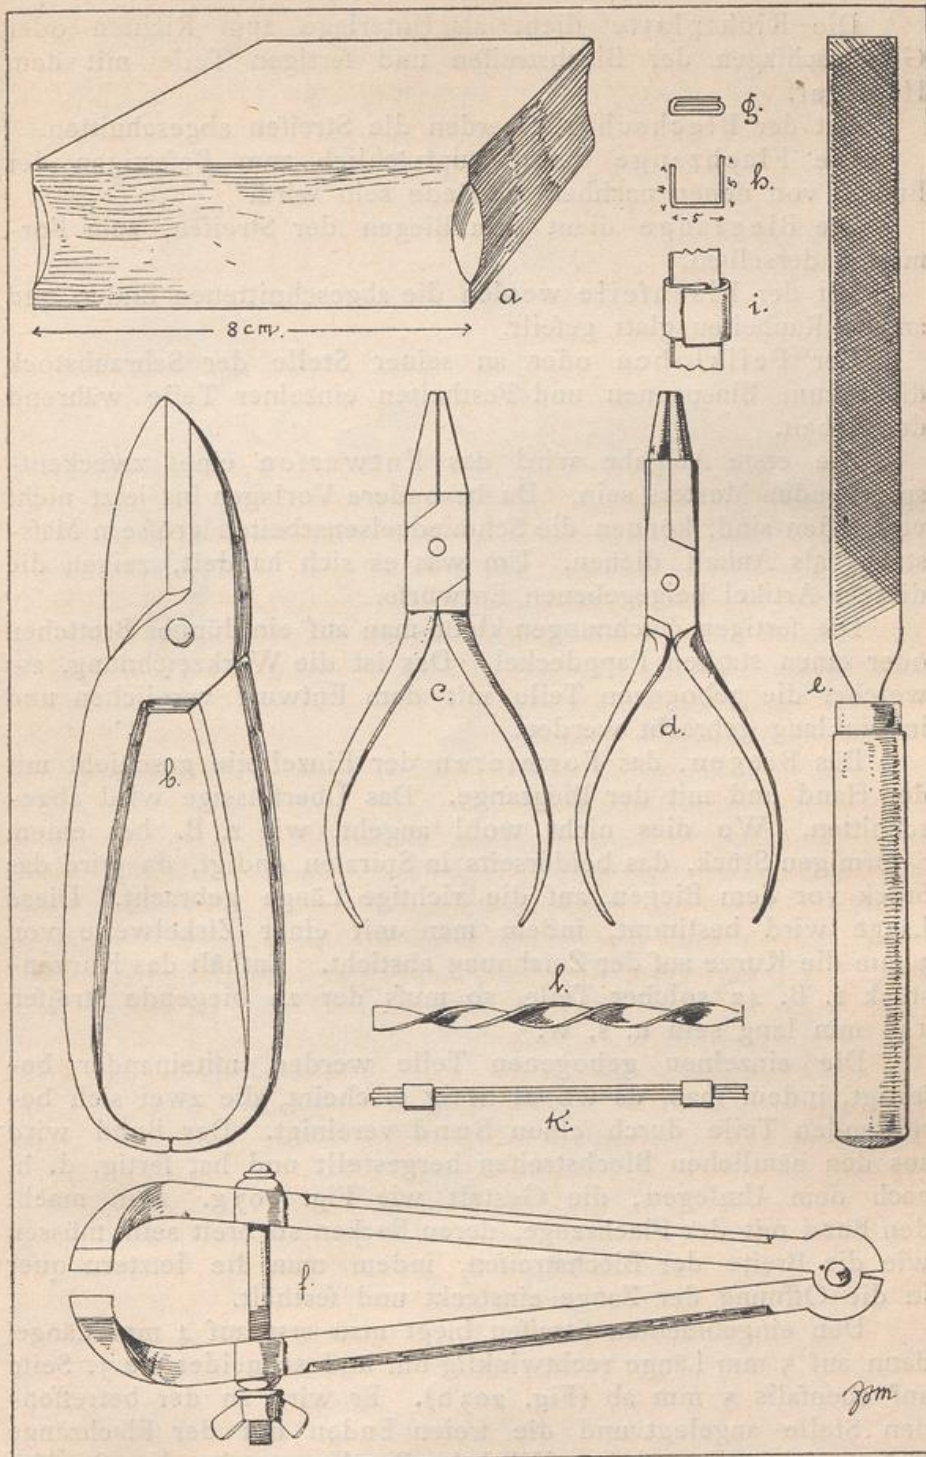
Werkzeuge für die Klein-Eisen-Arbeit.
